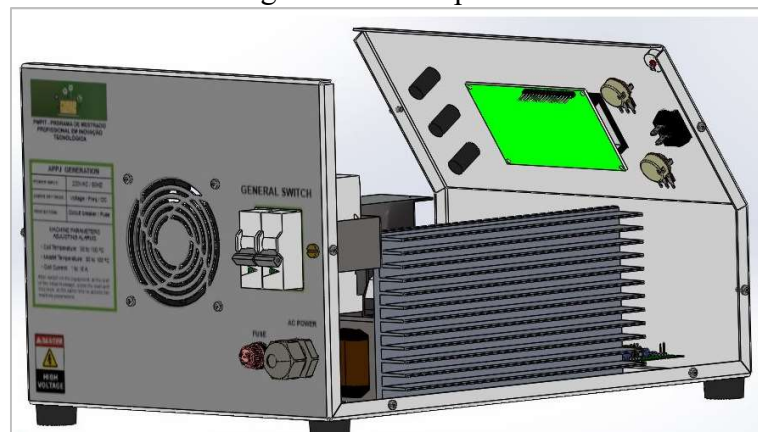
Desenho 3D do gabinete e componentes – Vista isométrica
